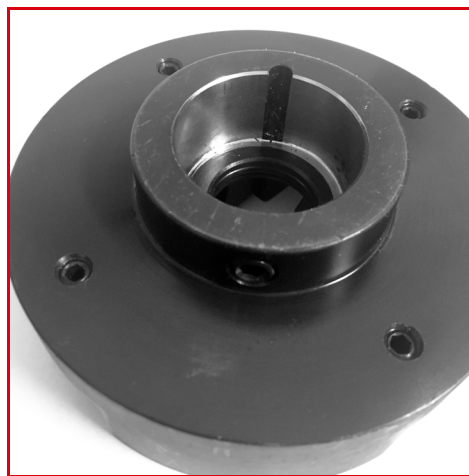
VIS DE BLOCAGE DU PORTE-OUTIL ET FENTE DE LA CLÉ
